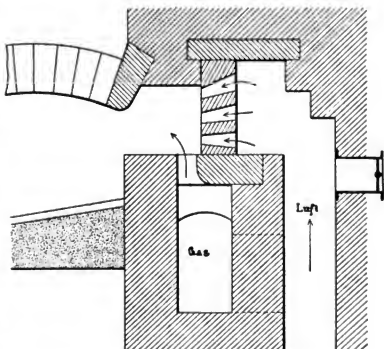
Gasrohrschweißofen mit Halbgasfeuerung.
